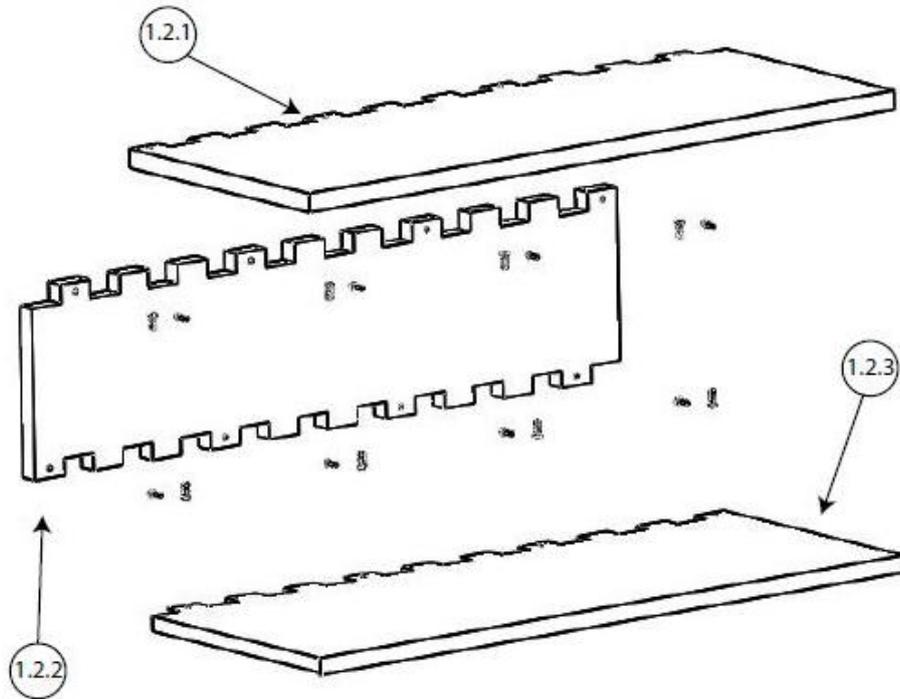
1.2.1 Madera 1. Dimensionado previo.
